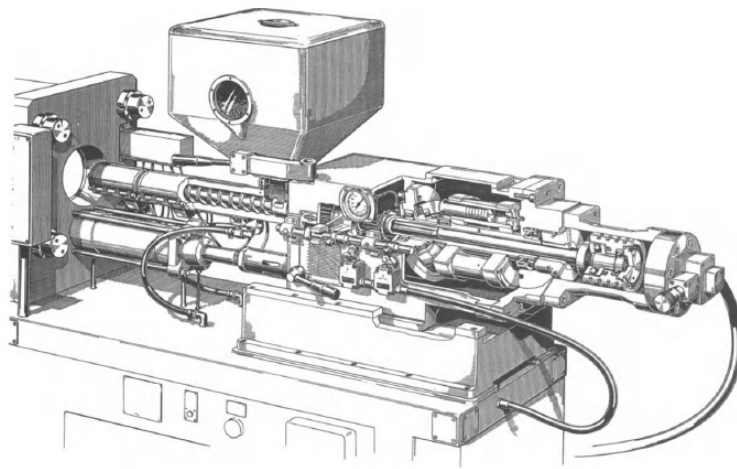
Vista de corte de una máquina de tornillo recíprocante [3].
